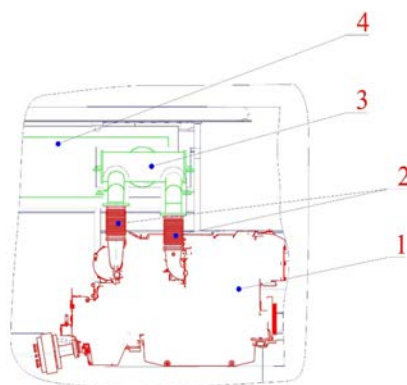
Схема компоновки СЕУ з ТАС (вид збоку): 1 – дизельний двигун, 2 сифонні компенсатори, 3 – патрубок газоходу, 4 – глушник-теплоаккумулятор
